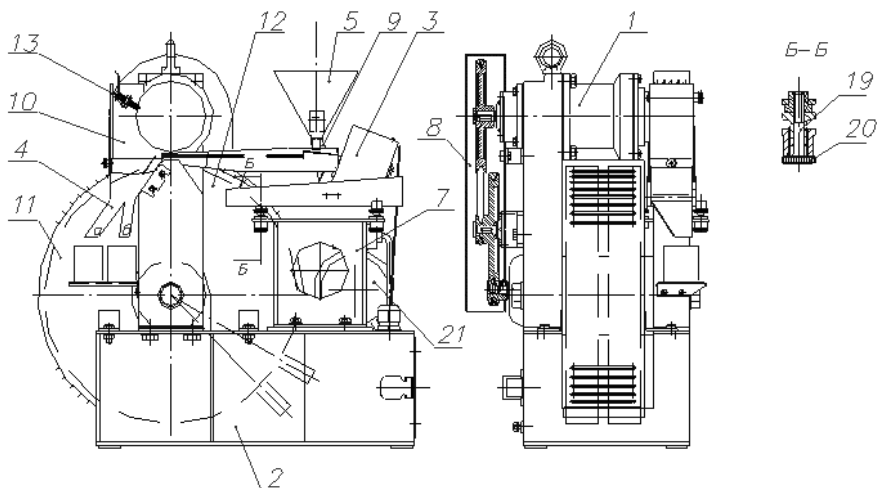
Схема лабораторного валкового электромагнитного сепаратора ЭВС 10/5:
